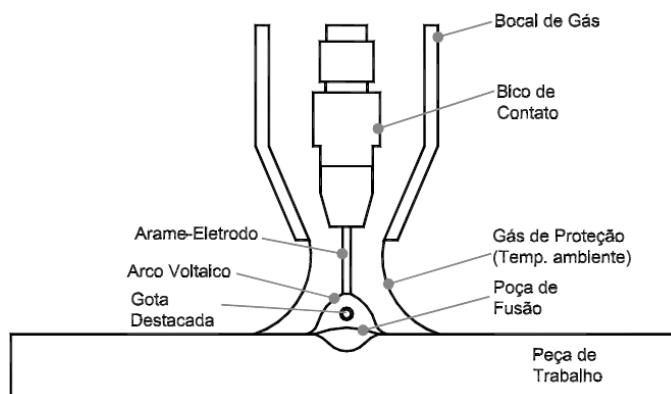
Desenho esquemático do processo de soldagem MIG/MAG (OLIVEIRA, 2006)
